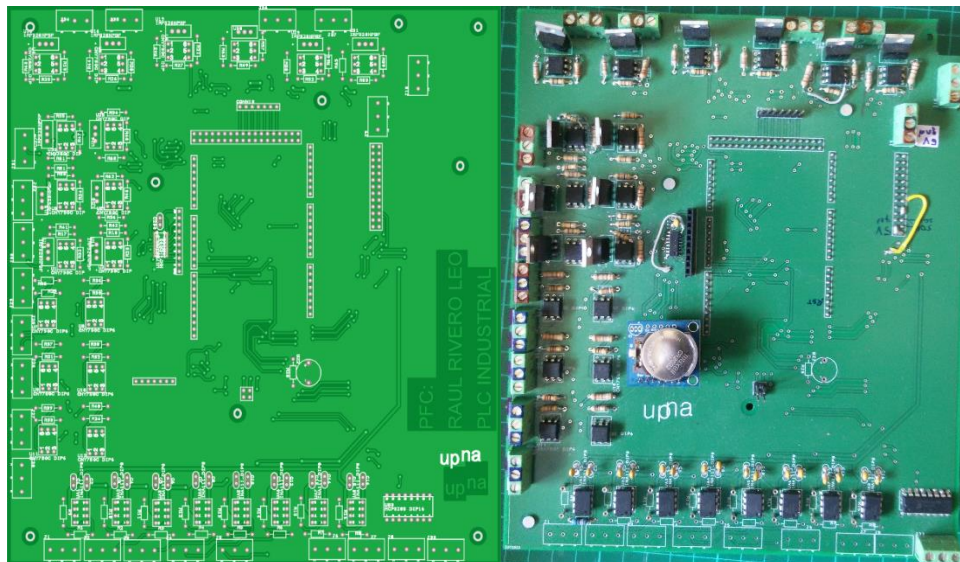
Layout superior completo extraído de EC [EuroCircuits] y resultado final de la PCB montada
